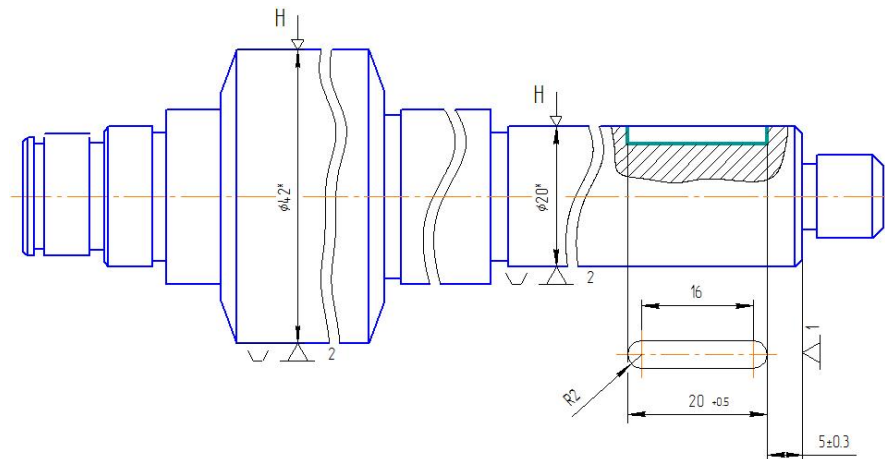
Схема базування деталі у верстатному пристрої
